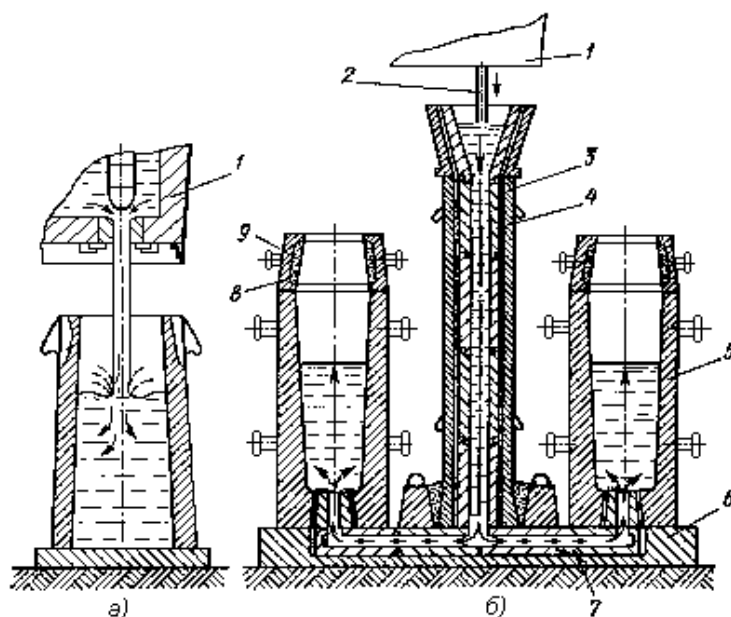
Разливка стали в изложницы: а – сверху; б – сифоном
